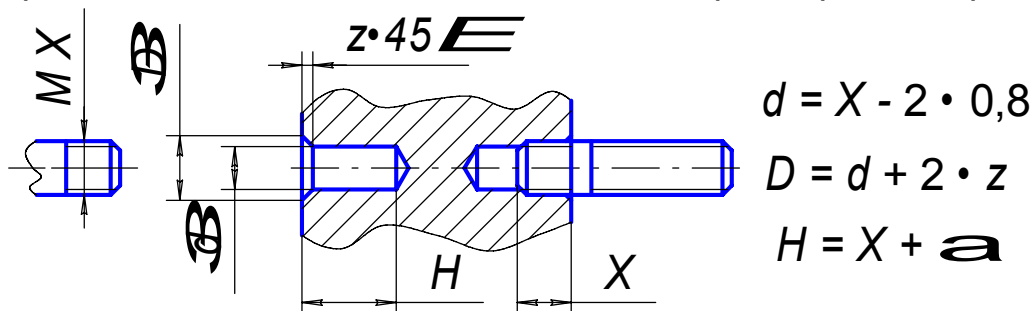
Параметры отверстия для установки шпильки в стальную деталь
